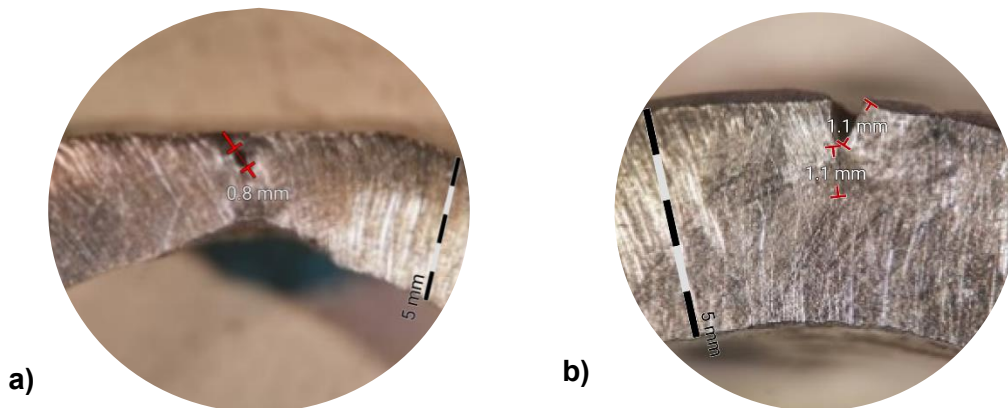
Soldaduras con discontinuidades: a) Carencia de penetración en soldadura homogénea a 125 A; b) Carencia de penetración y grieta de soldadura heterogénea a 80A
